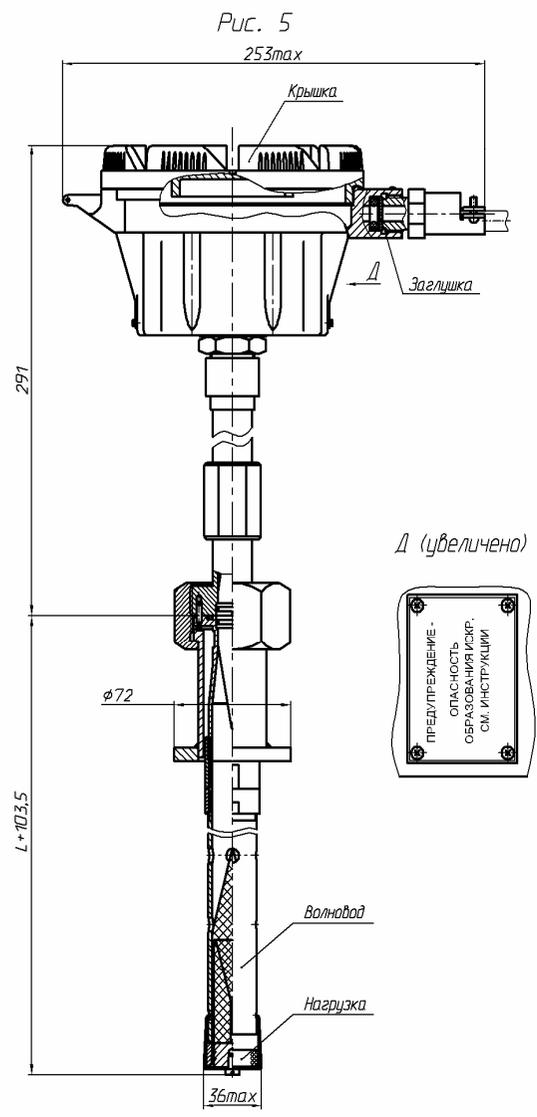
Габаритные и установочные размеры датчиков РДУЗ (лист 1)
